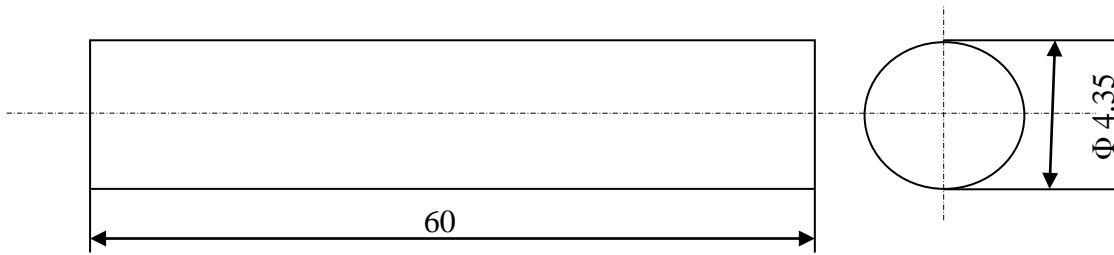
Dimensions et forme des éprouvettes utilisées.
